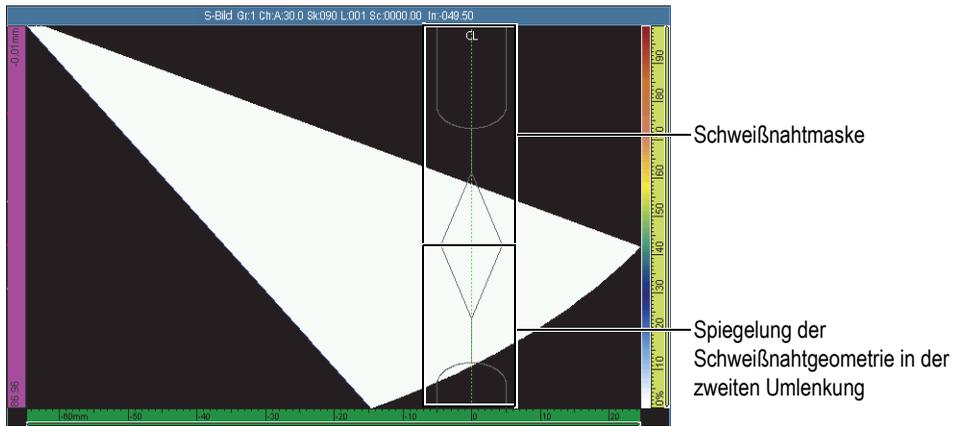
Schweißnahtmaske für Tulpe mit Gegenlage
